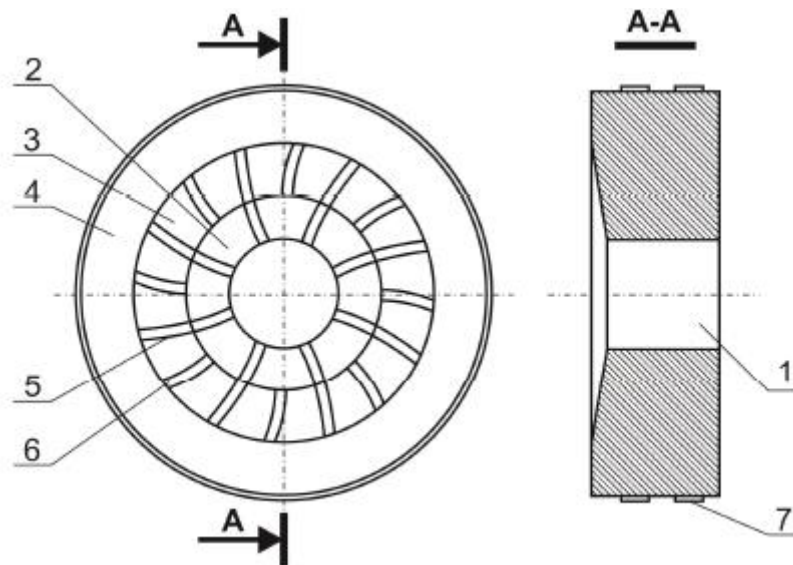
Жорнове каміння для млина з горизонтальною віссю обертання, розбивка робочої поверхні жорна: 1 – центральний отвір («вічко»); 2 - «двір» або «ковток»; 3 – пояс, що підводить; 4 – пояс, що розмелює; 5 – борозенка головна; 6 – борозенка другорядна, 7 – обруч.
